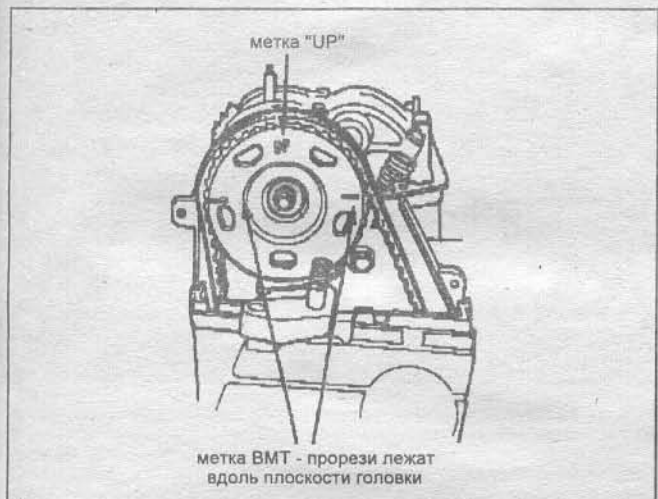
При монтаже шестерни следите чтобы маленькое отверстие (верхняя стрелка) или маркировка "UP" была вверху.
